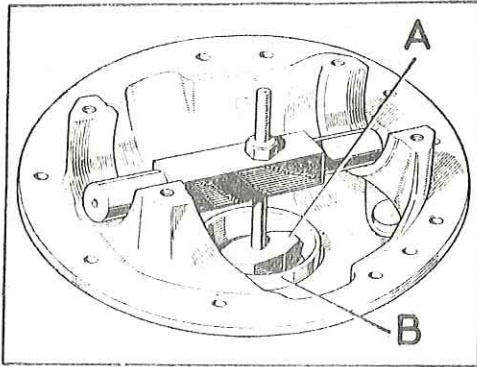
Desmontaje a presión de la pista exterior de rodamiento
